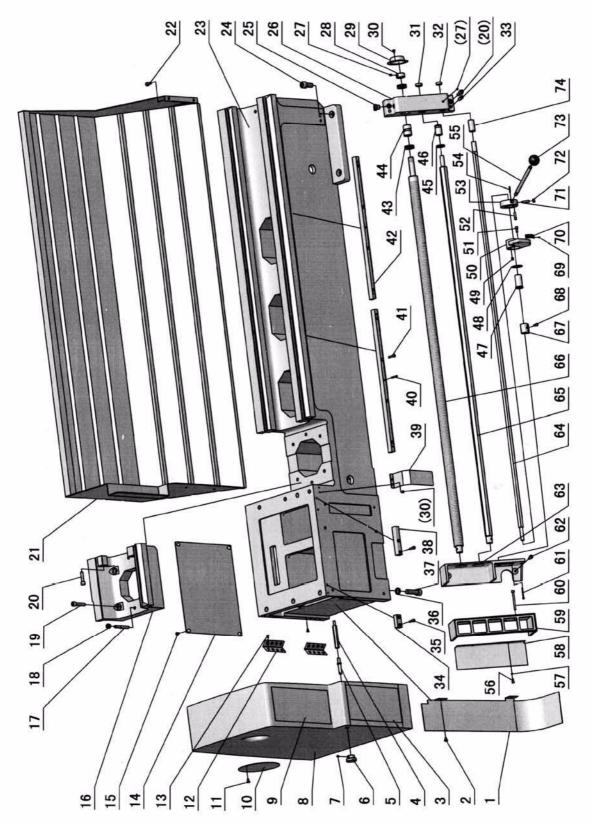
Maschinenbett, Vorschub, Abdeckungen - Machine bed, feed, covers
